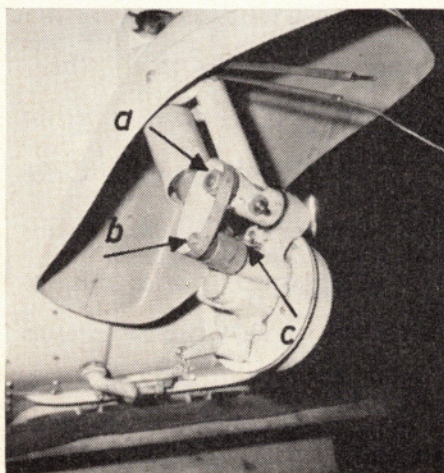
Zerlegen der Vorderradaufhängung: a = Mutter auf dem Schwingen-, b = Mutter auf dem Stoßdämpferankerbolzen, c = Klemmblech für Tachospirale.
